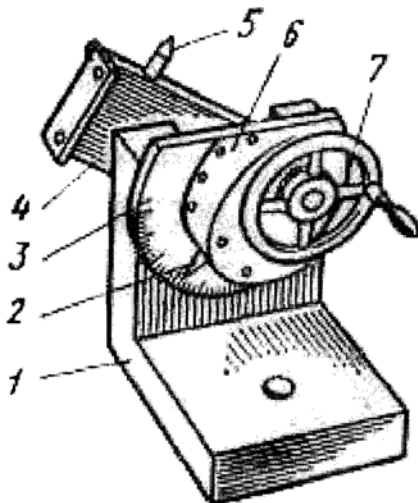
Нониусное приспособление с зубчатой передачей:
